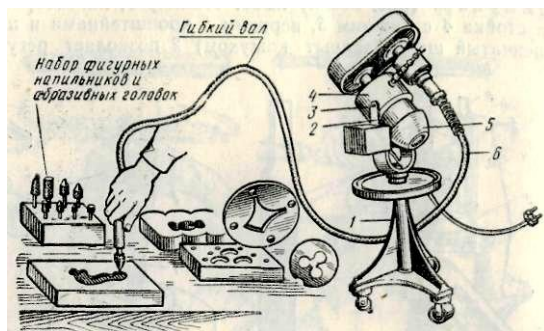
Передвижной опиловочно-зачистной станок ОЗС: 1 — стойка, 2 — вилка, 3 — шарниры, 4 — головка, 5 — электродвигатель, 6 — гибкий вал
